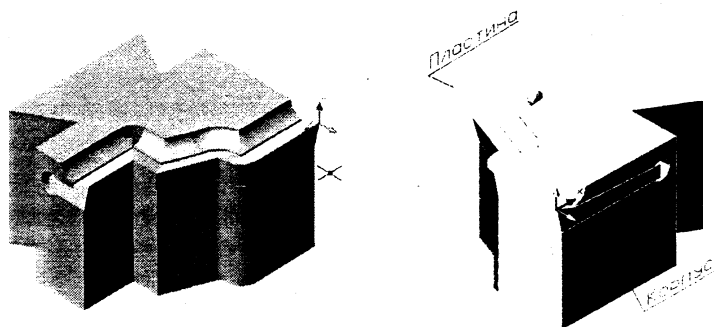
Фасонный призматический резец с пластиной, имеющей равные углы заточки вдоль режущей кромки
